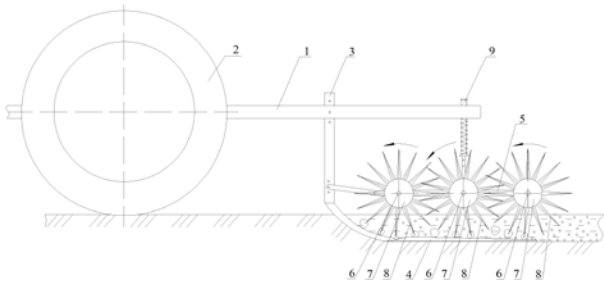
Схема удосконаленого культиватора для поверхневого обробітку ґрунту: 1 – рама; 2 – опорне колесо; 3 – стійка; 4 – лапа; 5 – полоз; 6 – вісь обертання; 7 – диск; 8 – вістря; 9 – пружний пристрій.
